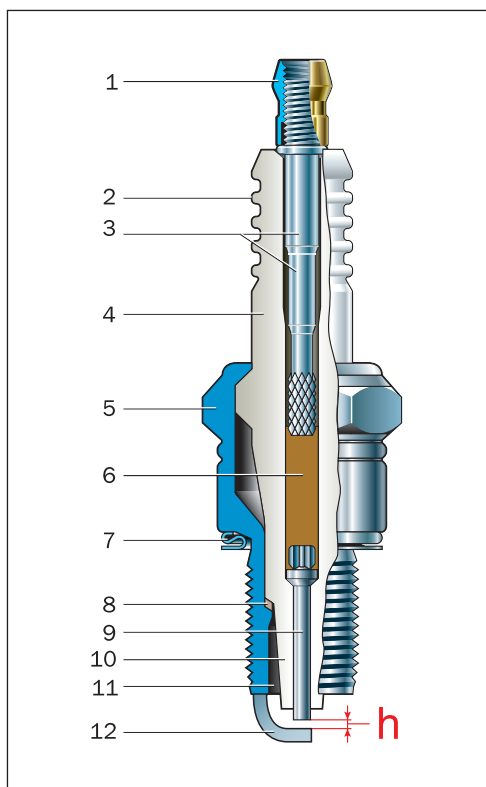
Свеча зажигания бензинового двигателя: 1 — контактная гайка; 2 — оребрение изолятора (барьеры для тока утечки); 3 — контактный стержень; 4 — керамический изолятор; 5 — металлический корпус; 6 — токопроводящий стеклогерметик; 7 — уплотнительное кольцо; 8 — теплоотводящая шайба; 9 — центральный электрод; 10 — тепловой конус изолятора; 11 — рабочая камера; 12 — боковой электрод «масса»; h — искровой зазор
